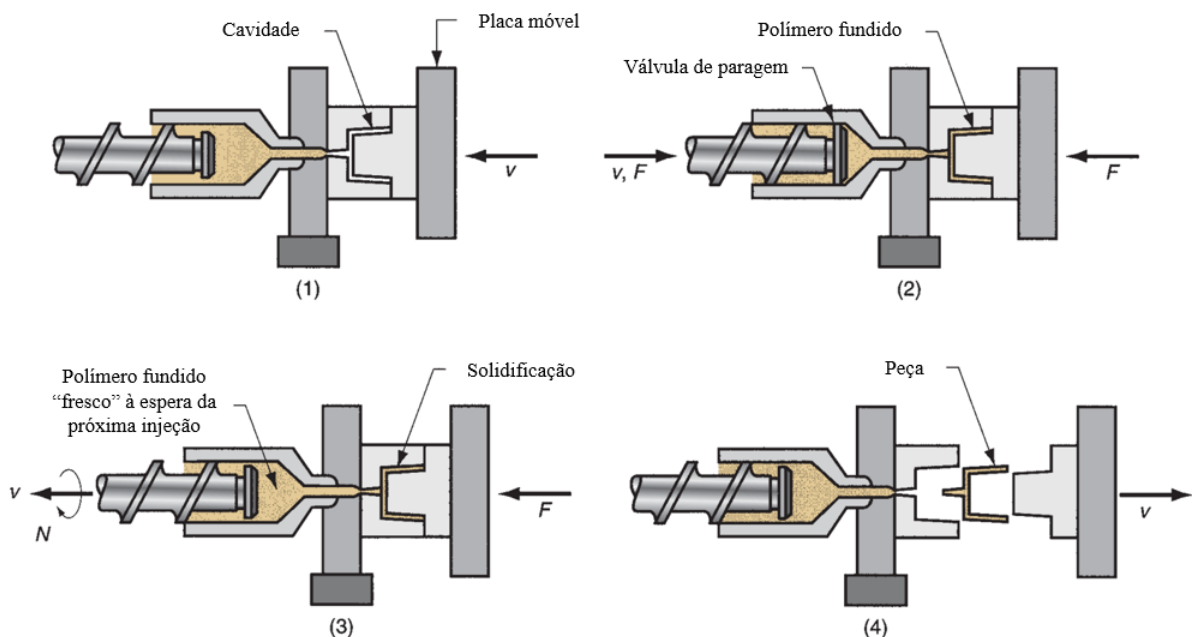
Esquema representativo do processo de moldagem por injeção (Adaptado de [57]).
